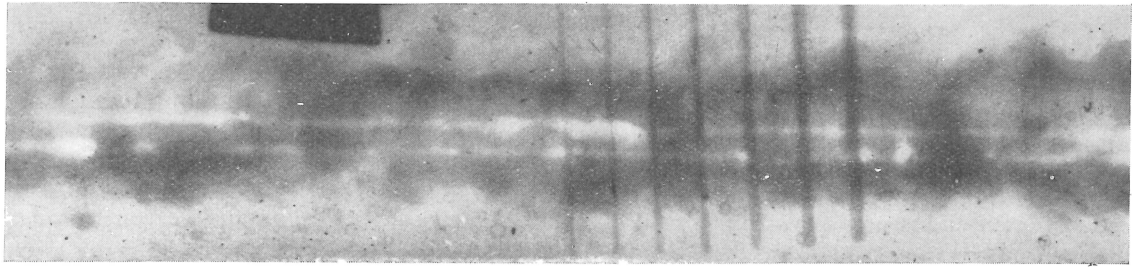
Radiographie d'une soudure en X (épaisseur 20 mm) : manque de pénétration double.
